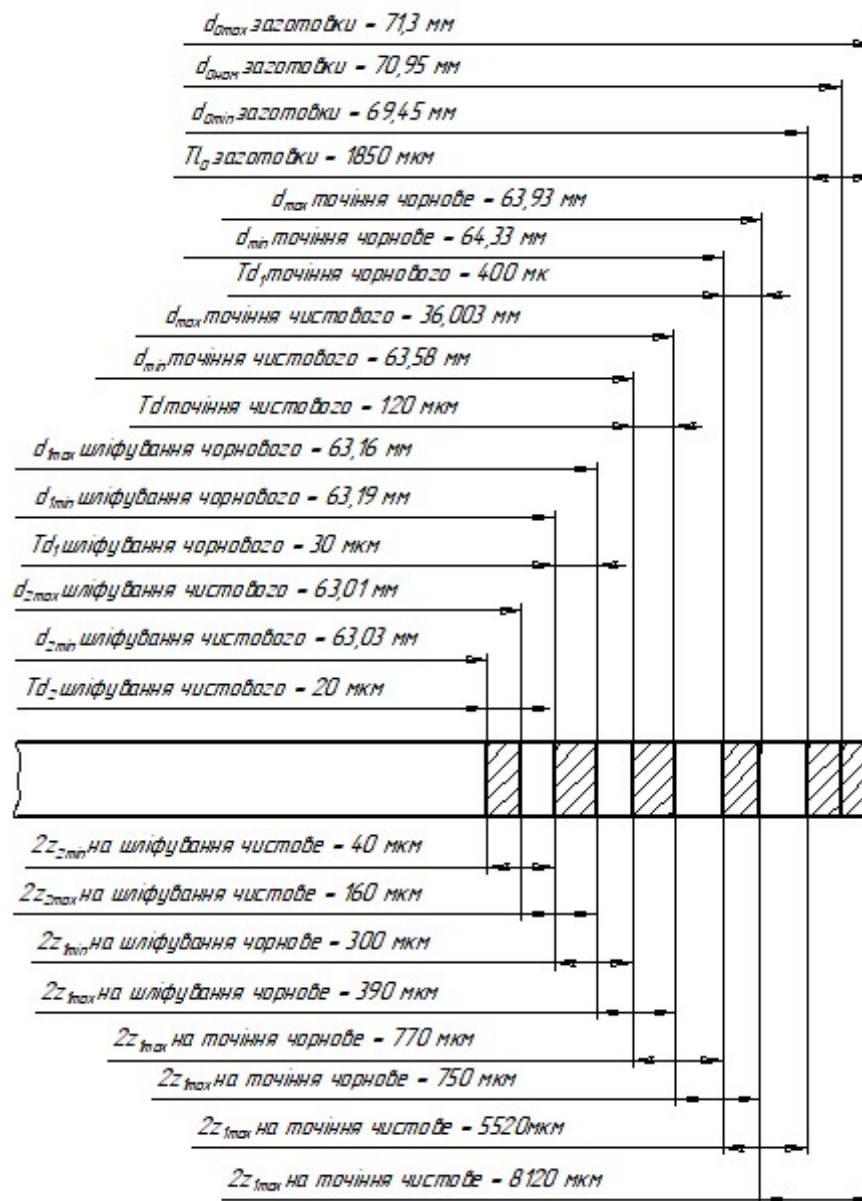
Схема графічного розташування припусків і допусків на обробку циліндричної поверхні штока  $\phi 63 h8$
